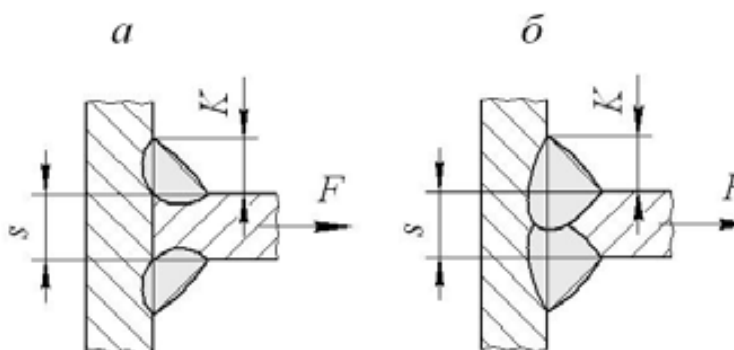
Тавровые соединения, работающие на растяжение: а – выполненное угловыми швами; б – выполненное стыковым швом
